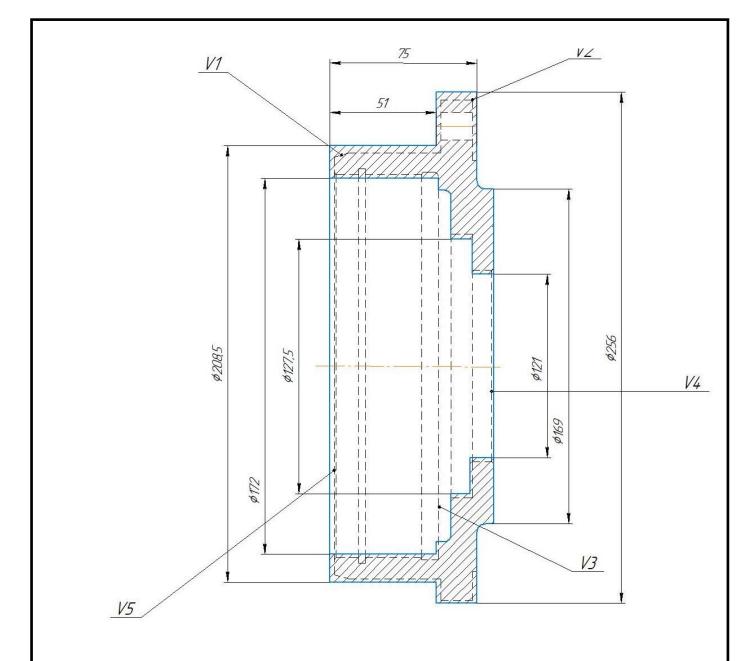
Эскиз заготовки детали Крышка ДЗ-98.1006.086
